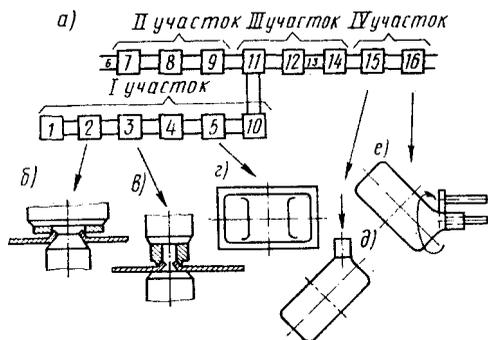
Схема автоматической линии изготовления топливных баков
